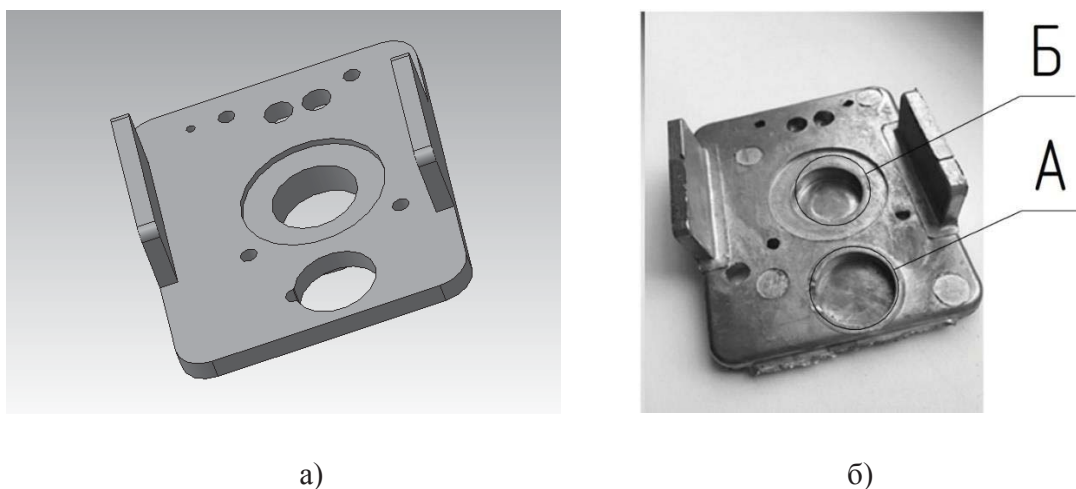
Отливка «Крышка» а) 3D модель; б) реальная отливка
